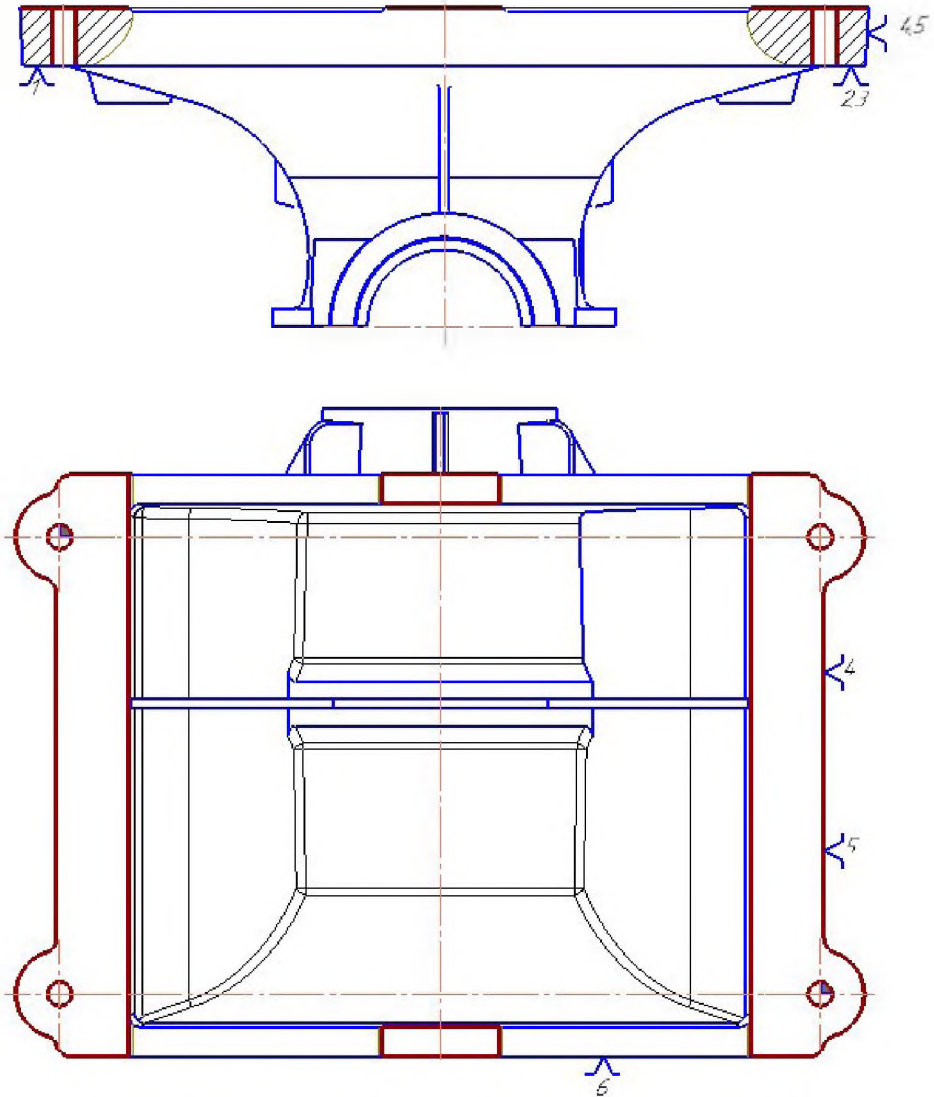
Теоретична схема базування деталі «Корпус» по технологічним базам
